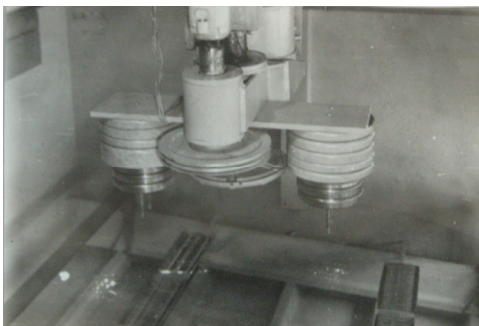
Фотография станка для магнитно-абразивной обработки шариков
